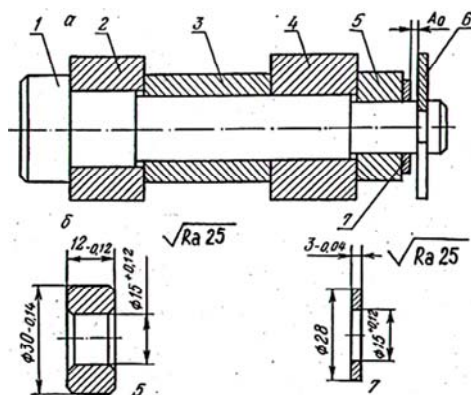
Сборочная единица (а) с неподвижным компенсатором и входящие в нее детали (б):
